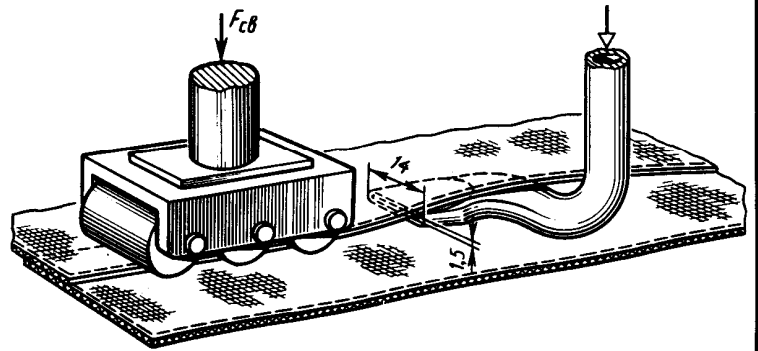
Схема непрерывной сварки пленки газовым теплоносителем
